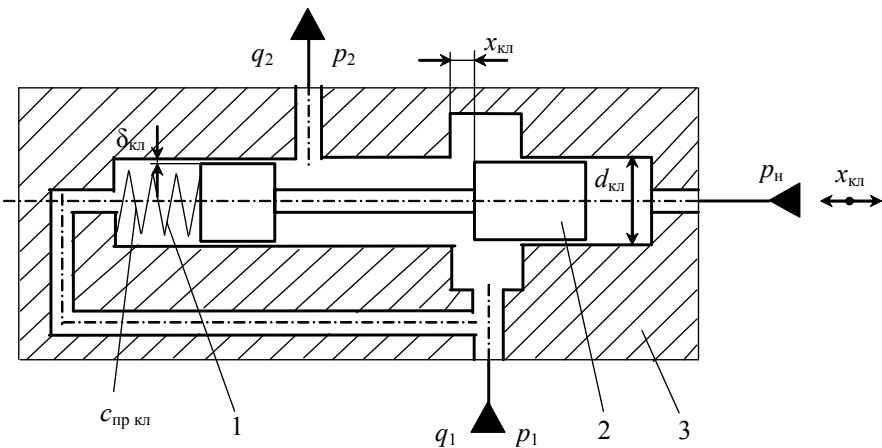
Розрахункова схема клапана тиску: 1 – пружина; 2 – золотник; 3 – корпус.
